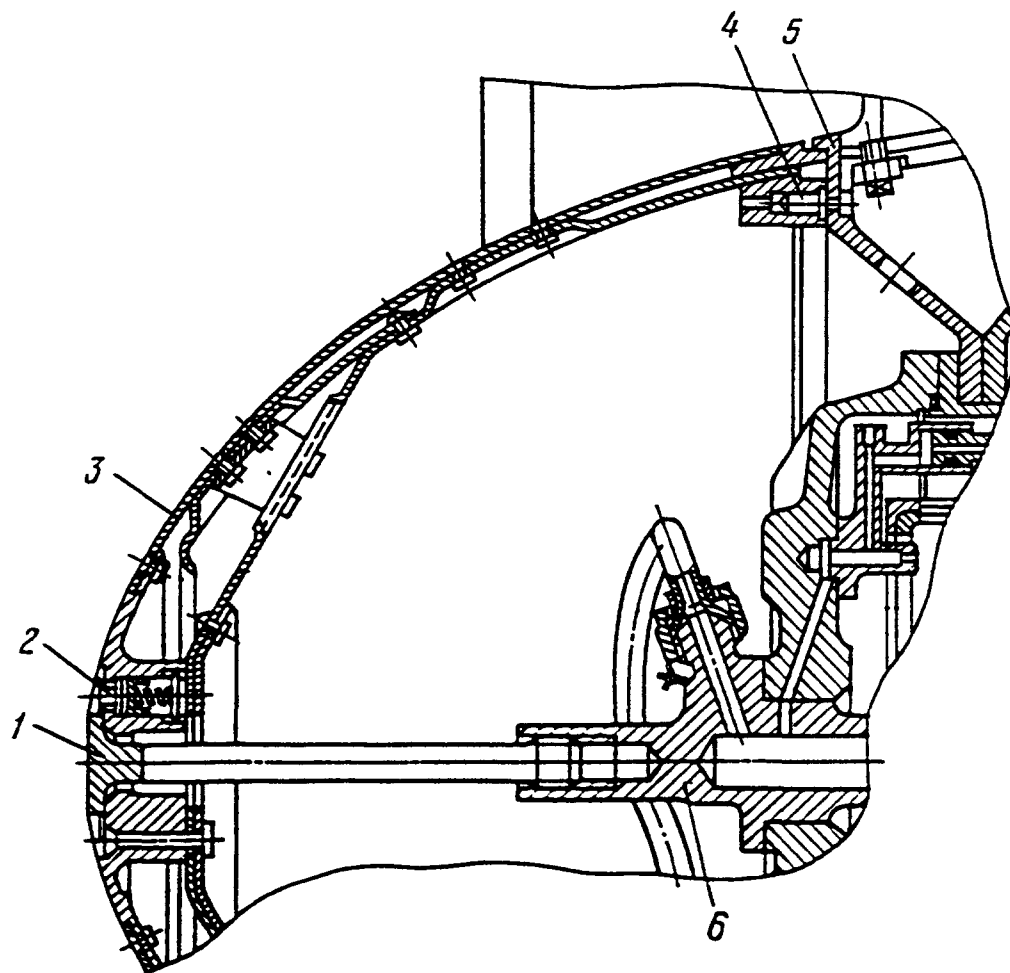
Монтаж обтекателя на входной корпус двигателя:
